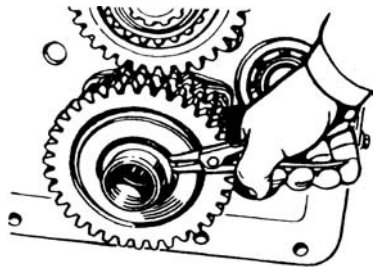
Спрессовка промежуточной шестерни понижающего редуктора, замена подшипников № 212.
